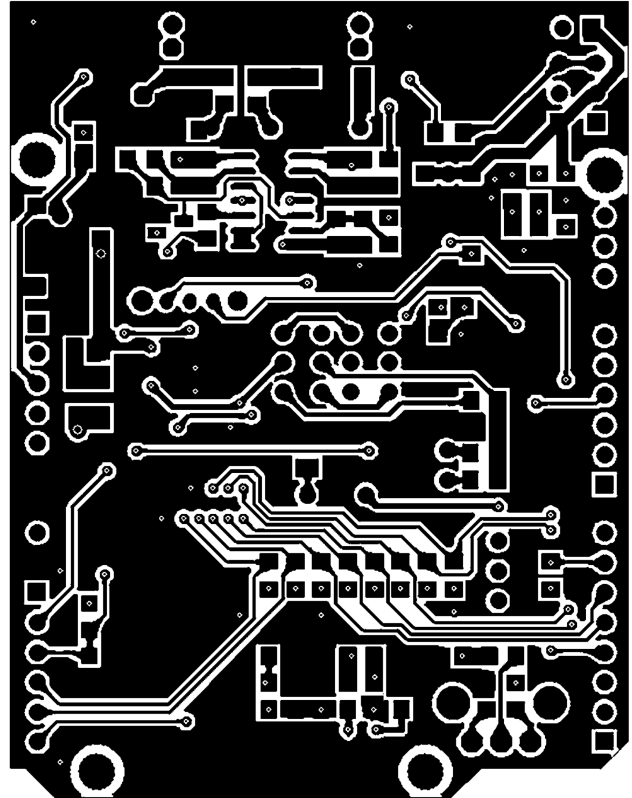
Cara de pistas inferior de la PCB para la realización preferida.
